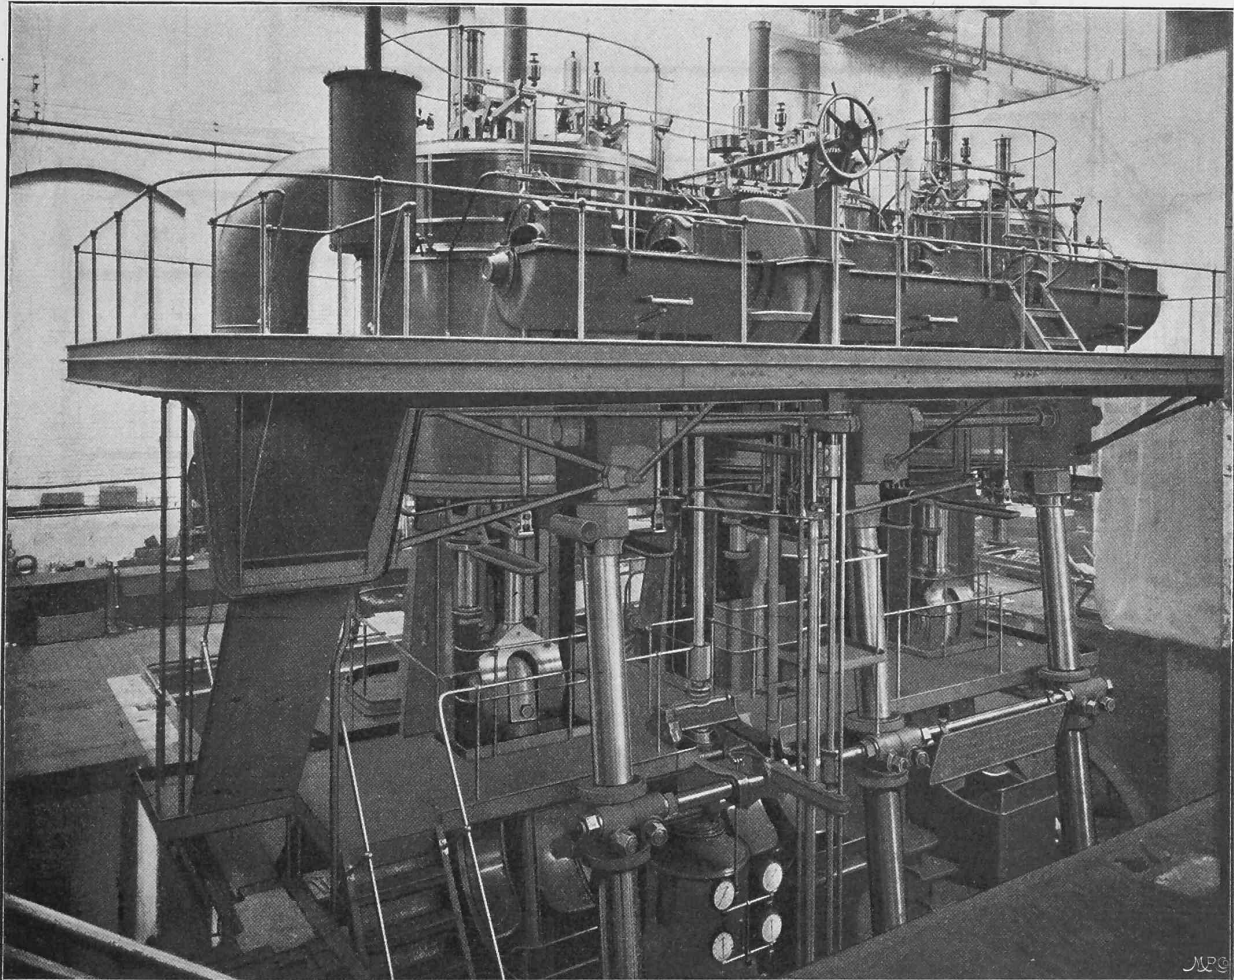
Vertikale dreizylindrige Verbund-Ventil-Dampfmaschine von 5000 P. S. erbaut von Gebrüder Sulzer in Winterthur. Vorderansicht der Maschine in der Montierhalle zu Winterthur.
